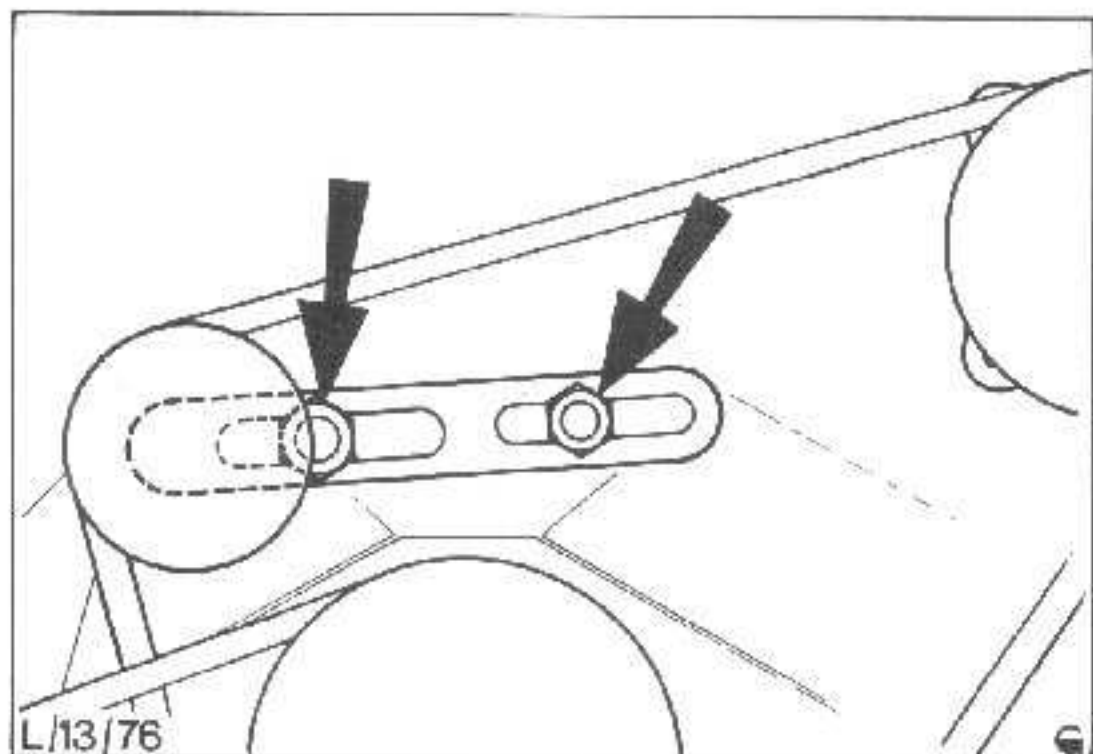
Befestigungsschrauben der Umlenkrolle (V6-Motor)
